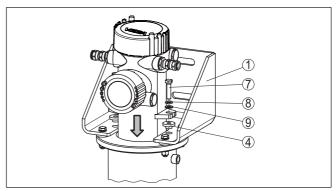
Montaje del sensor - POINTRAC - versión corta
